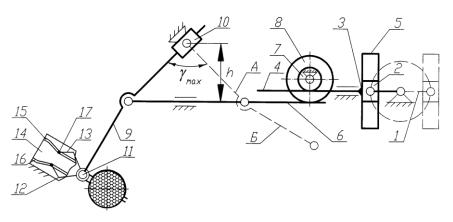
Кинематическая схема устройства захвата и переноса изделий [4]
